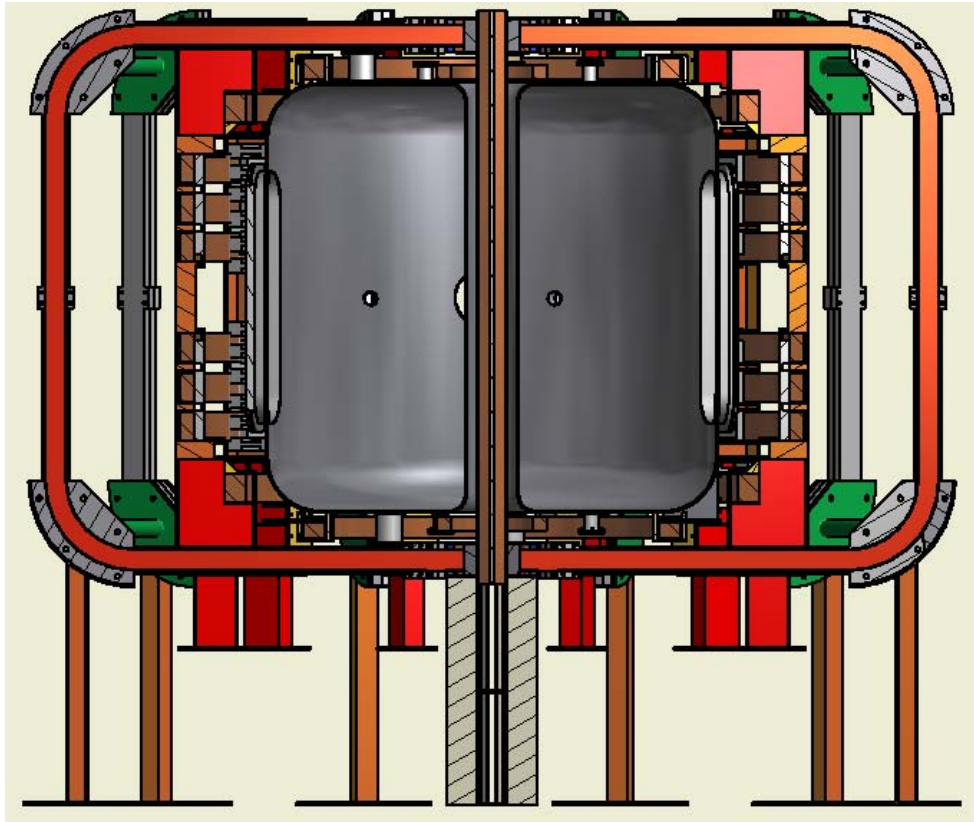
Plano de levantamiento del tokamak TMX-1, con corte transversal en plano z-x.
